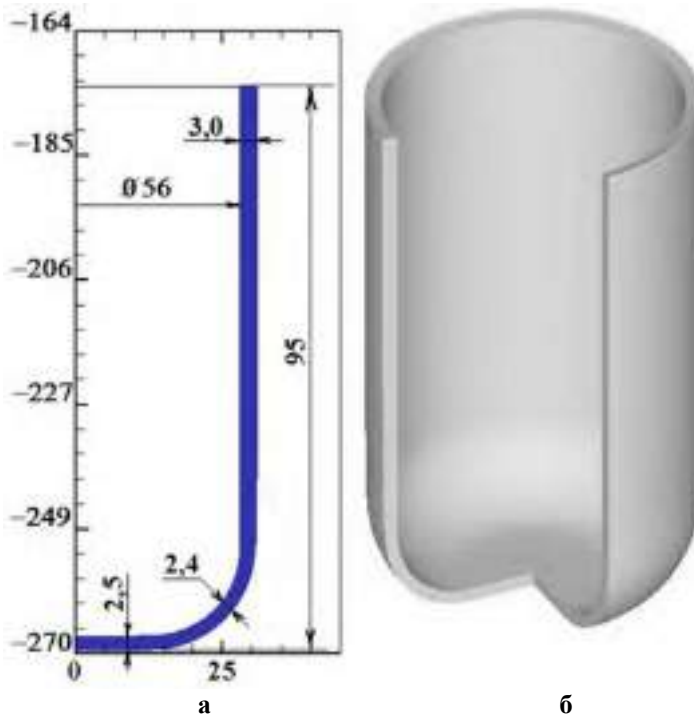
Форма та розміри в міліметрах zdeформованої заготовки та загальний вигляд виробу в розрізі
